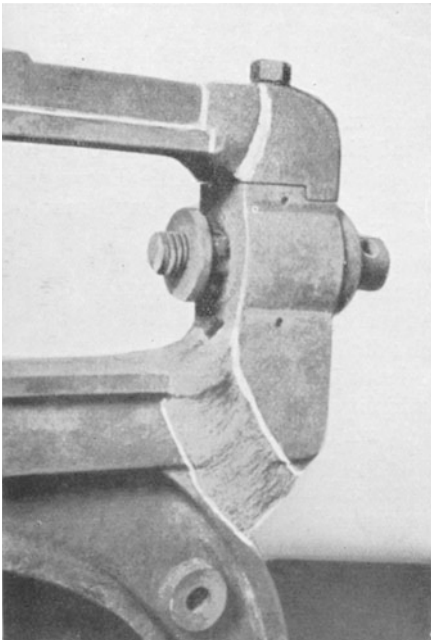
Schweißung am Ständer einer Gummiwalze.
